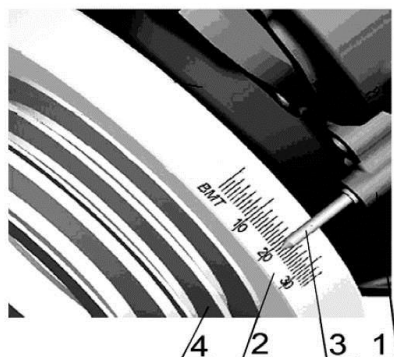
Установка угла опережения впрыска топлива: 1 – крышка распределительных шестерен; 2 – шкала; 3 – штифт установочный; 4 – шкив
